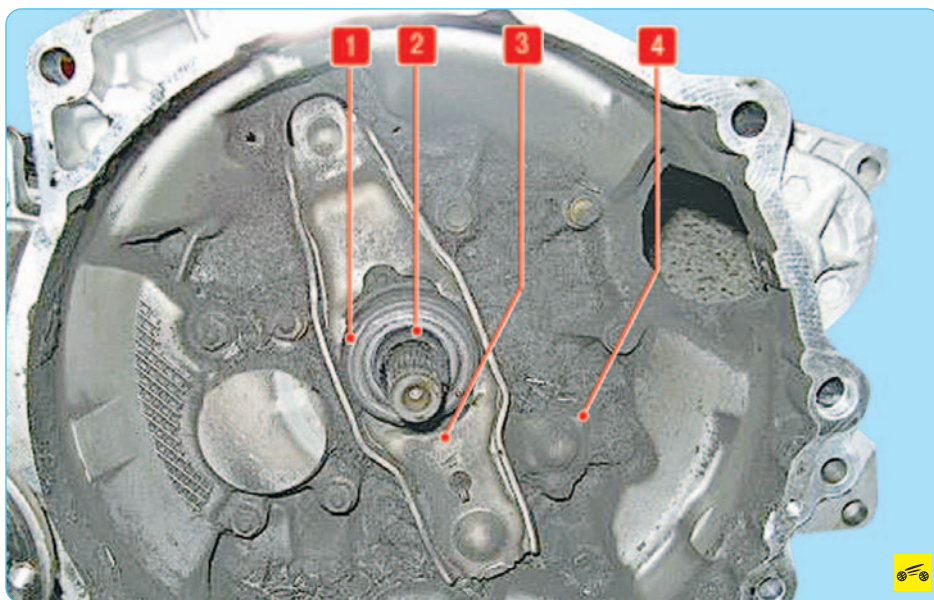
Картер сцепления: 1 – подшипник выключения сцепления; 2 – направляющая втулка подшипника выключения сцепления; 3 – вилка выключения сцепления; 4 – картер сцепления
